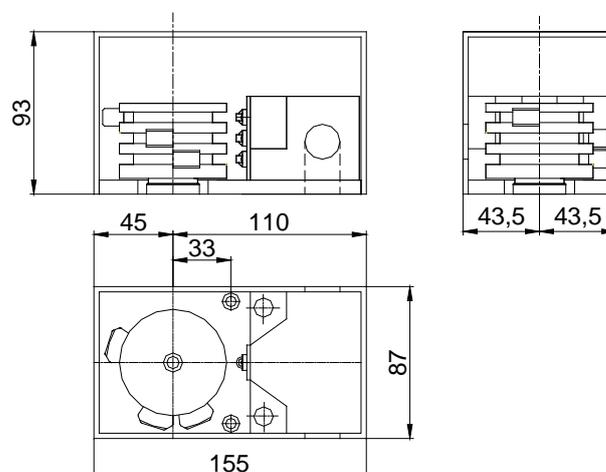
Dimensioni di ingombro del gruppo FC3
